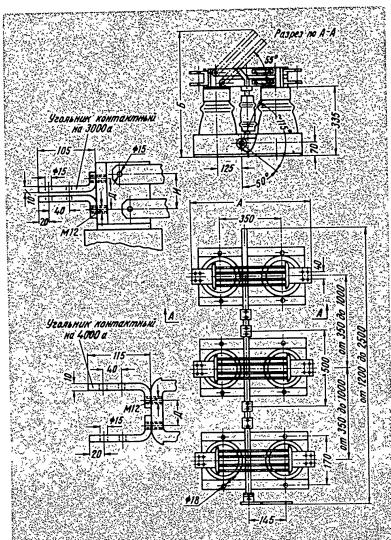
Габаритные и установочные размеры разъединителей серии РВУ.
